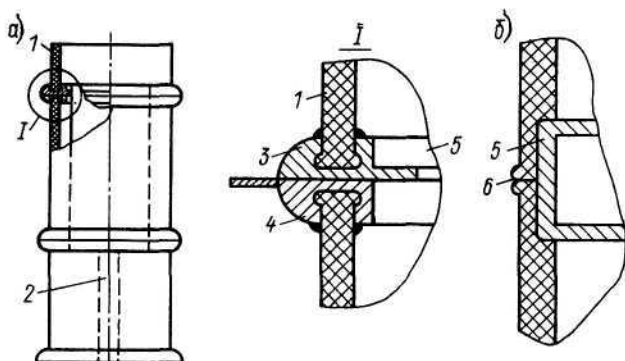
Выключатели коаксиального типа и горячего формирования (а) и сварного типа (б)
